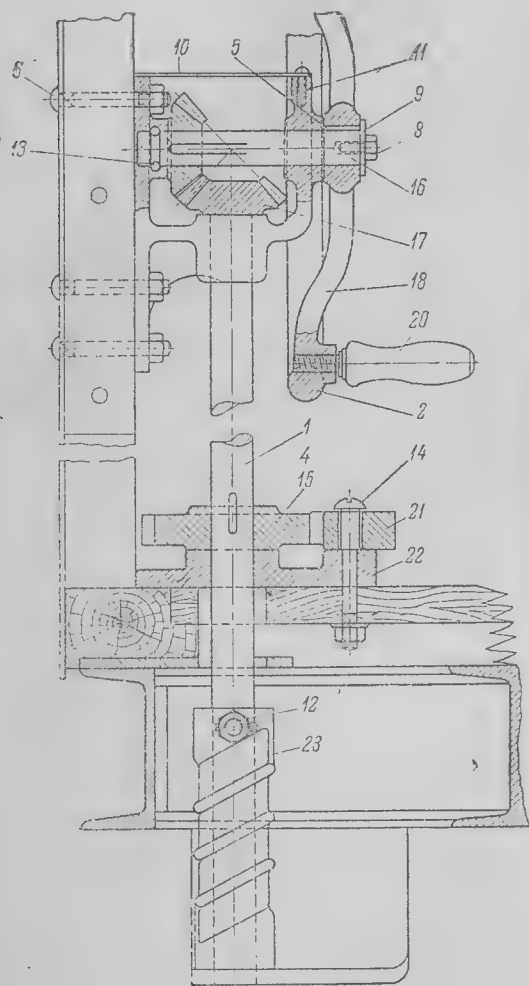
Ручной привод тормоза сцепного вагона на свободных осях.
